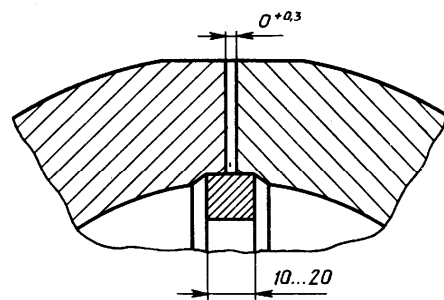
Сборка стыка арматуры под сварку электронным лучом
